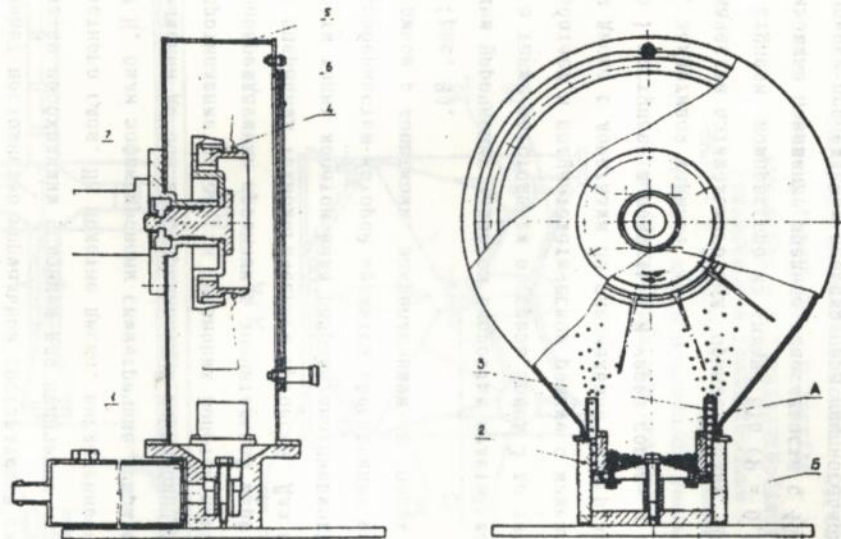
Схема установки для пневмодробеистой упрочнения шариками лопаток компрессора: I - ресивер; 2 - дробесборник; 3 - сопло; 4 - диск; 5 - корпус; 6 - сетчатый экран, 7 - исполнительный механизм постоянного тока типа МЗК - 2.
